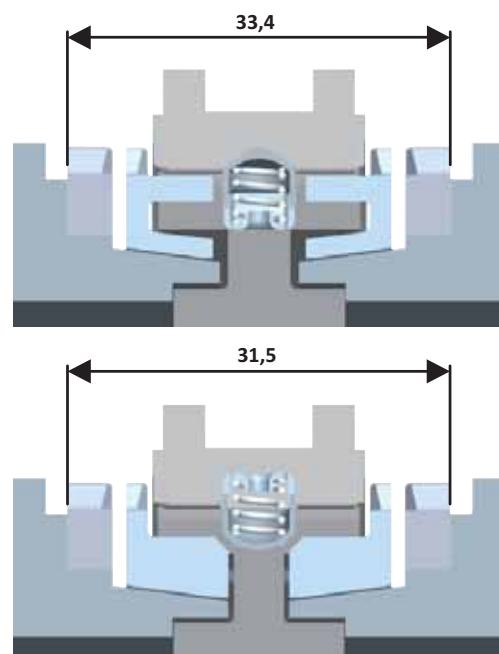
Oben: Ein Synchronisationssystem mit flachem Druckstück. Unten: Reduzierte Getriebelänge durch „Strut-in-Sleeve“ Design.
